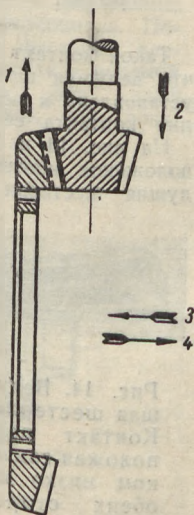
Направление сдвига шестерен при регулировке зацепления.
